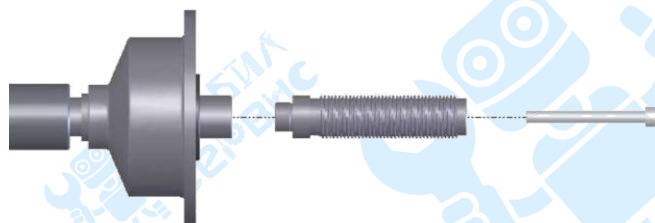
Вал типа конус для колес с центральным отверстием.
